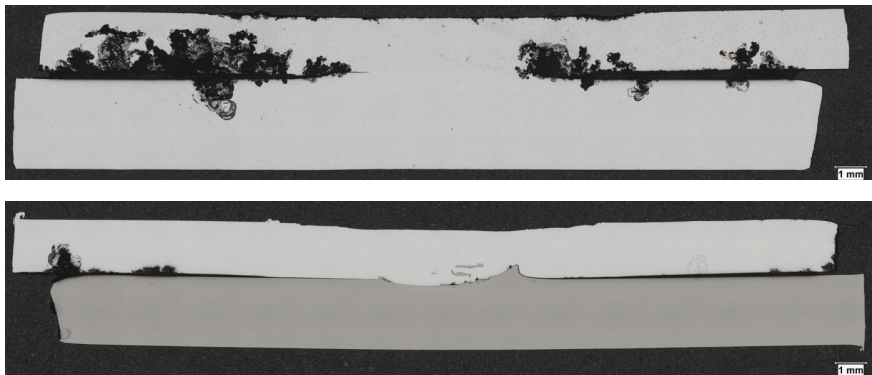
车辆经过 10 万公里公路行驶后, 车轮和挡泥板之间经搅拌摩擦焊接 (friction-stir welded, 简称 FSW) 而成的多材料装配剖视图。上: 在 AA7000 系列与 AA6000 系列的 FSW 装配中, 缝隙腐蚀为主要的腐蚀方式。下: 在 AA5000 系列与不锈钢 300 系列的 FSW 装配中, 电偶腐蚀为主要的腐蚀方式。
